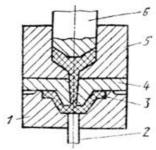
Схема пресс-формы литьевого прессования: 1 – матрица; 2 – выталкиватель; 3 – изделие; 4 – пуансон; 5 – загрузочная камера; 6 – пуансон загрузочной камеры
